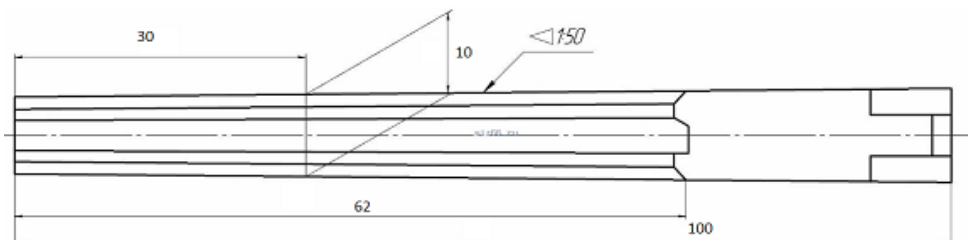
развертка коническая ГОСТ 2372-0015
